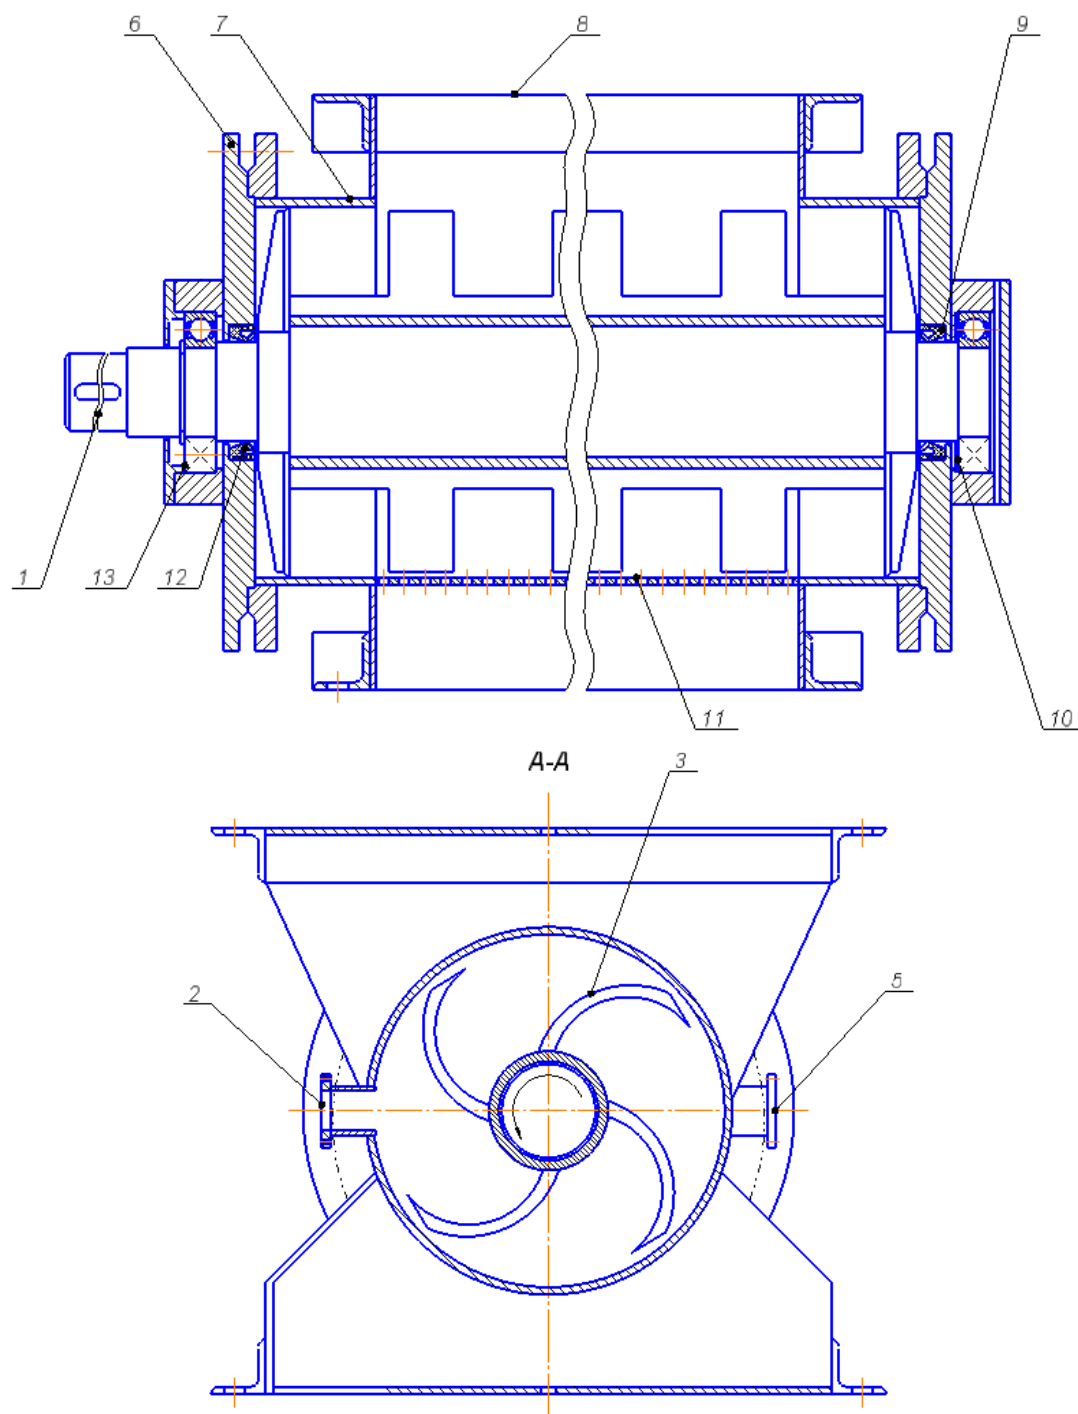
Модернізований завантажувальний пристрій сушарки
